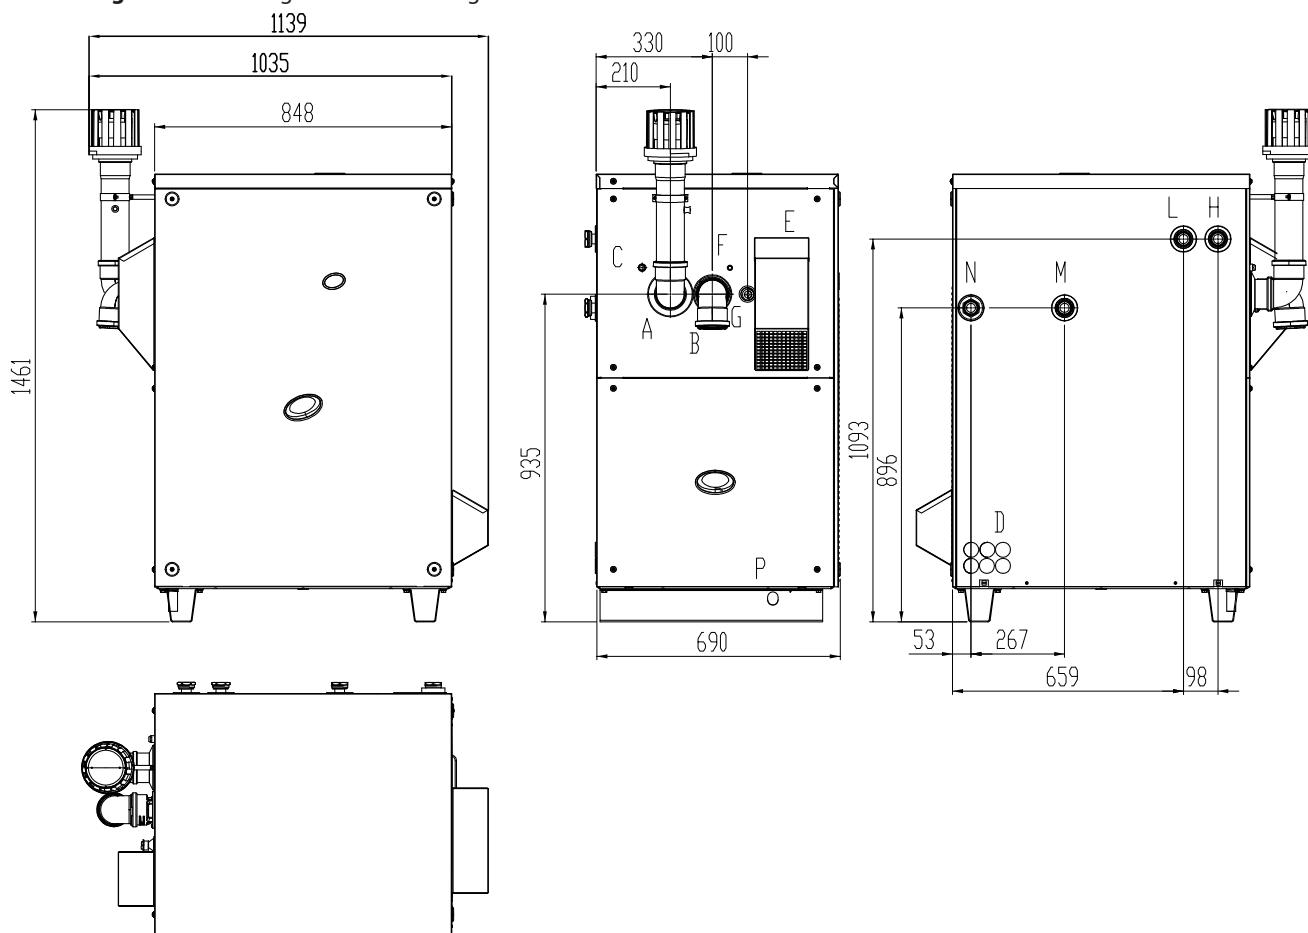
Zeichnung Innenabmessungen GAHP-GS/WS
